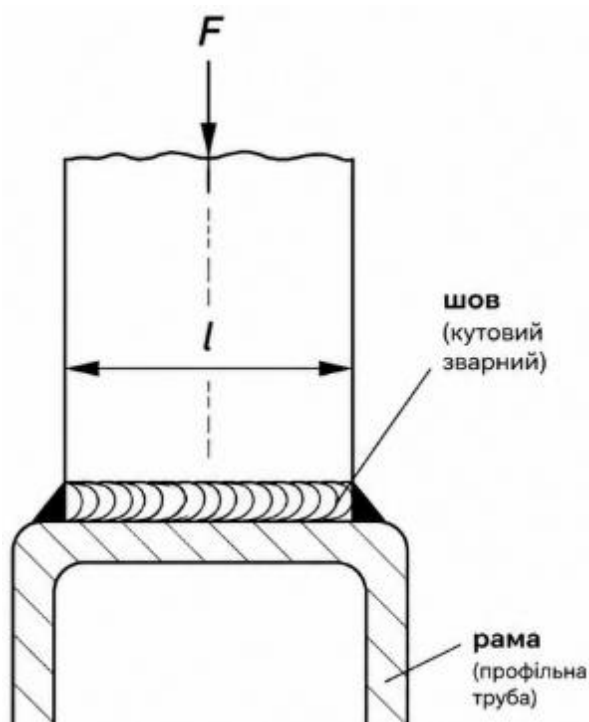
Схема кутового таврового зварного з'єднання
